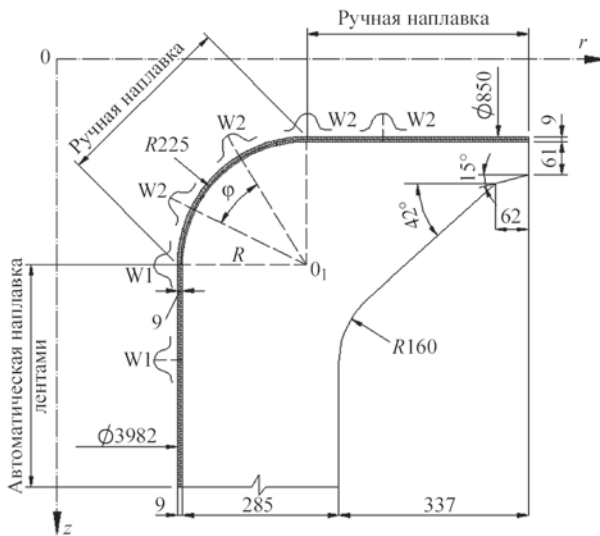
Схема патрубковой зоны корпуса реактора и расположение участков с различными способами наплавки
